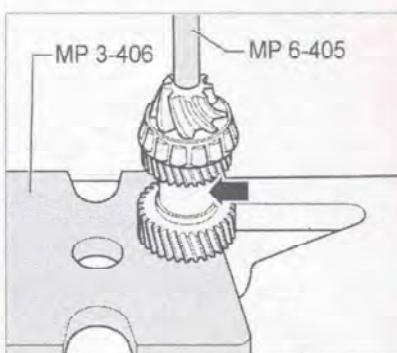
Напрессуйте шестерню 3-й передачи на вал с помощью специального инструмента.
